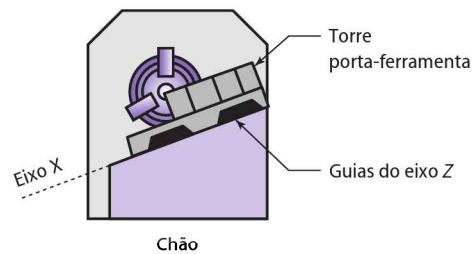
Um barramento de um torno com inclinação possui um eixo X inclinado em relação ao chão para melhorar a remoção de cavaco e o acesso do operador às ferramentas.
